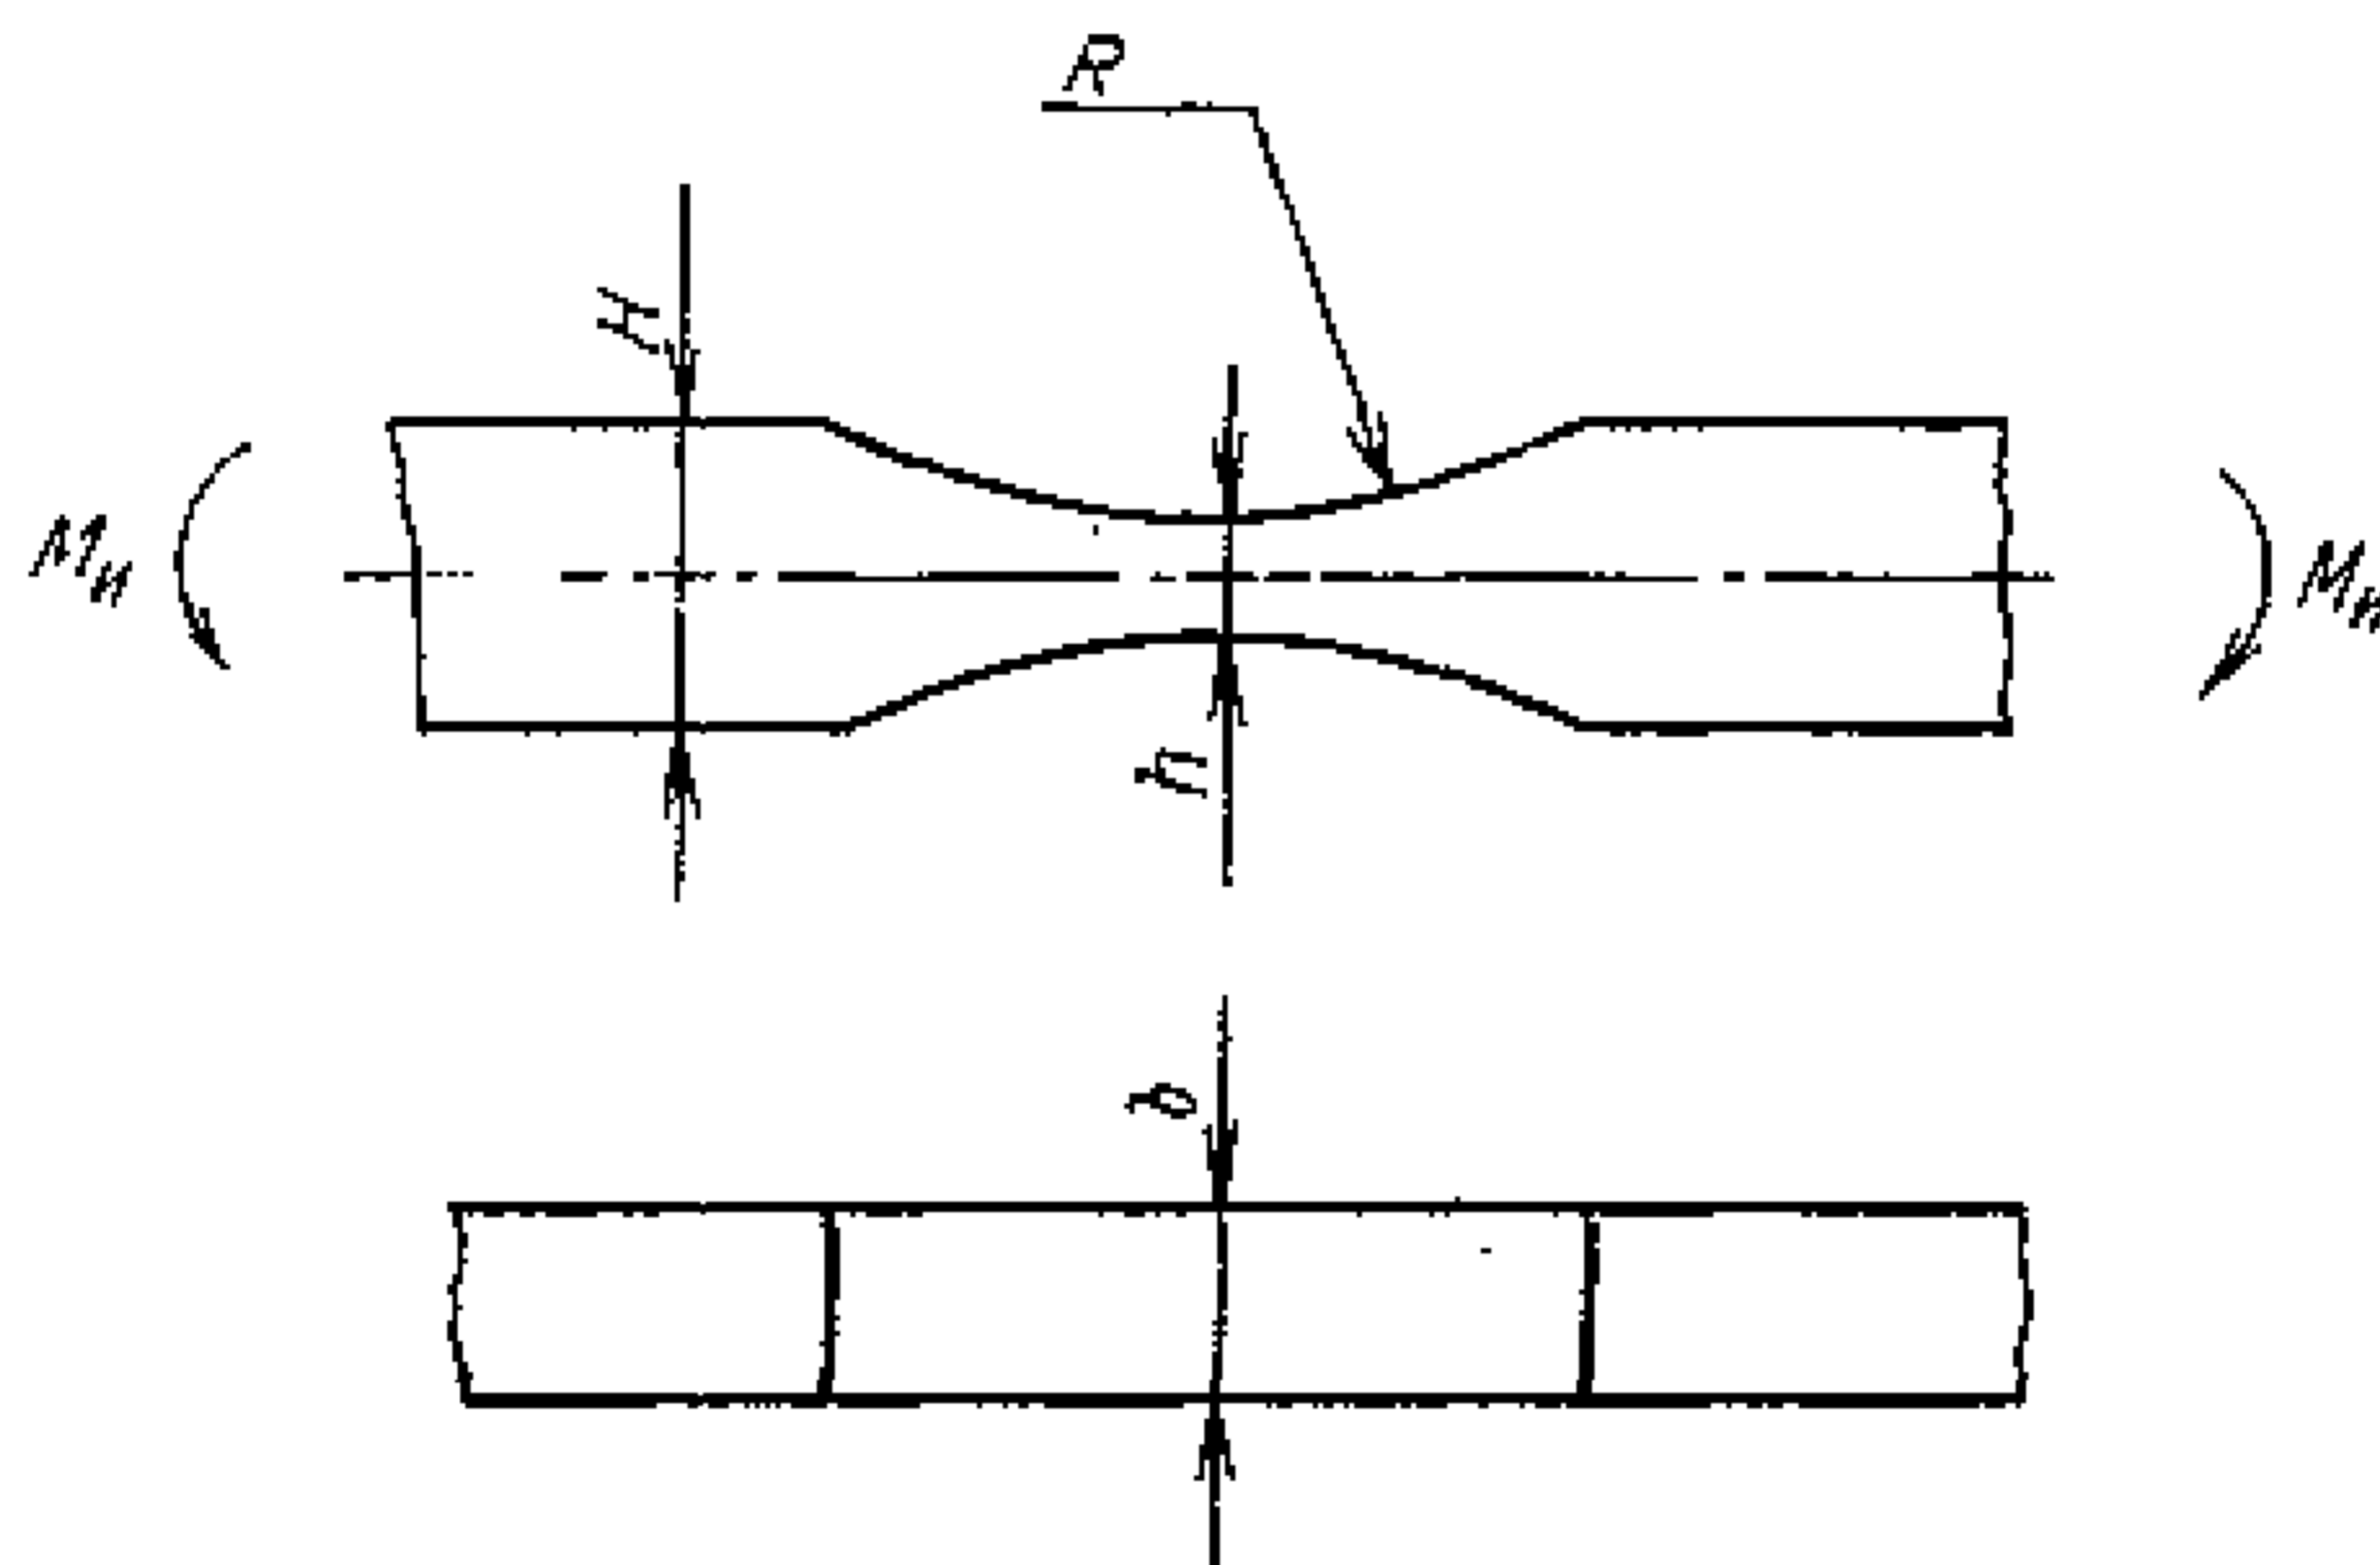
Форма и размеры рабочей части образца для испытаний при повторном изгибе:
